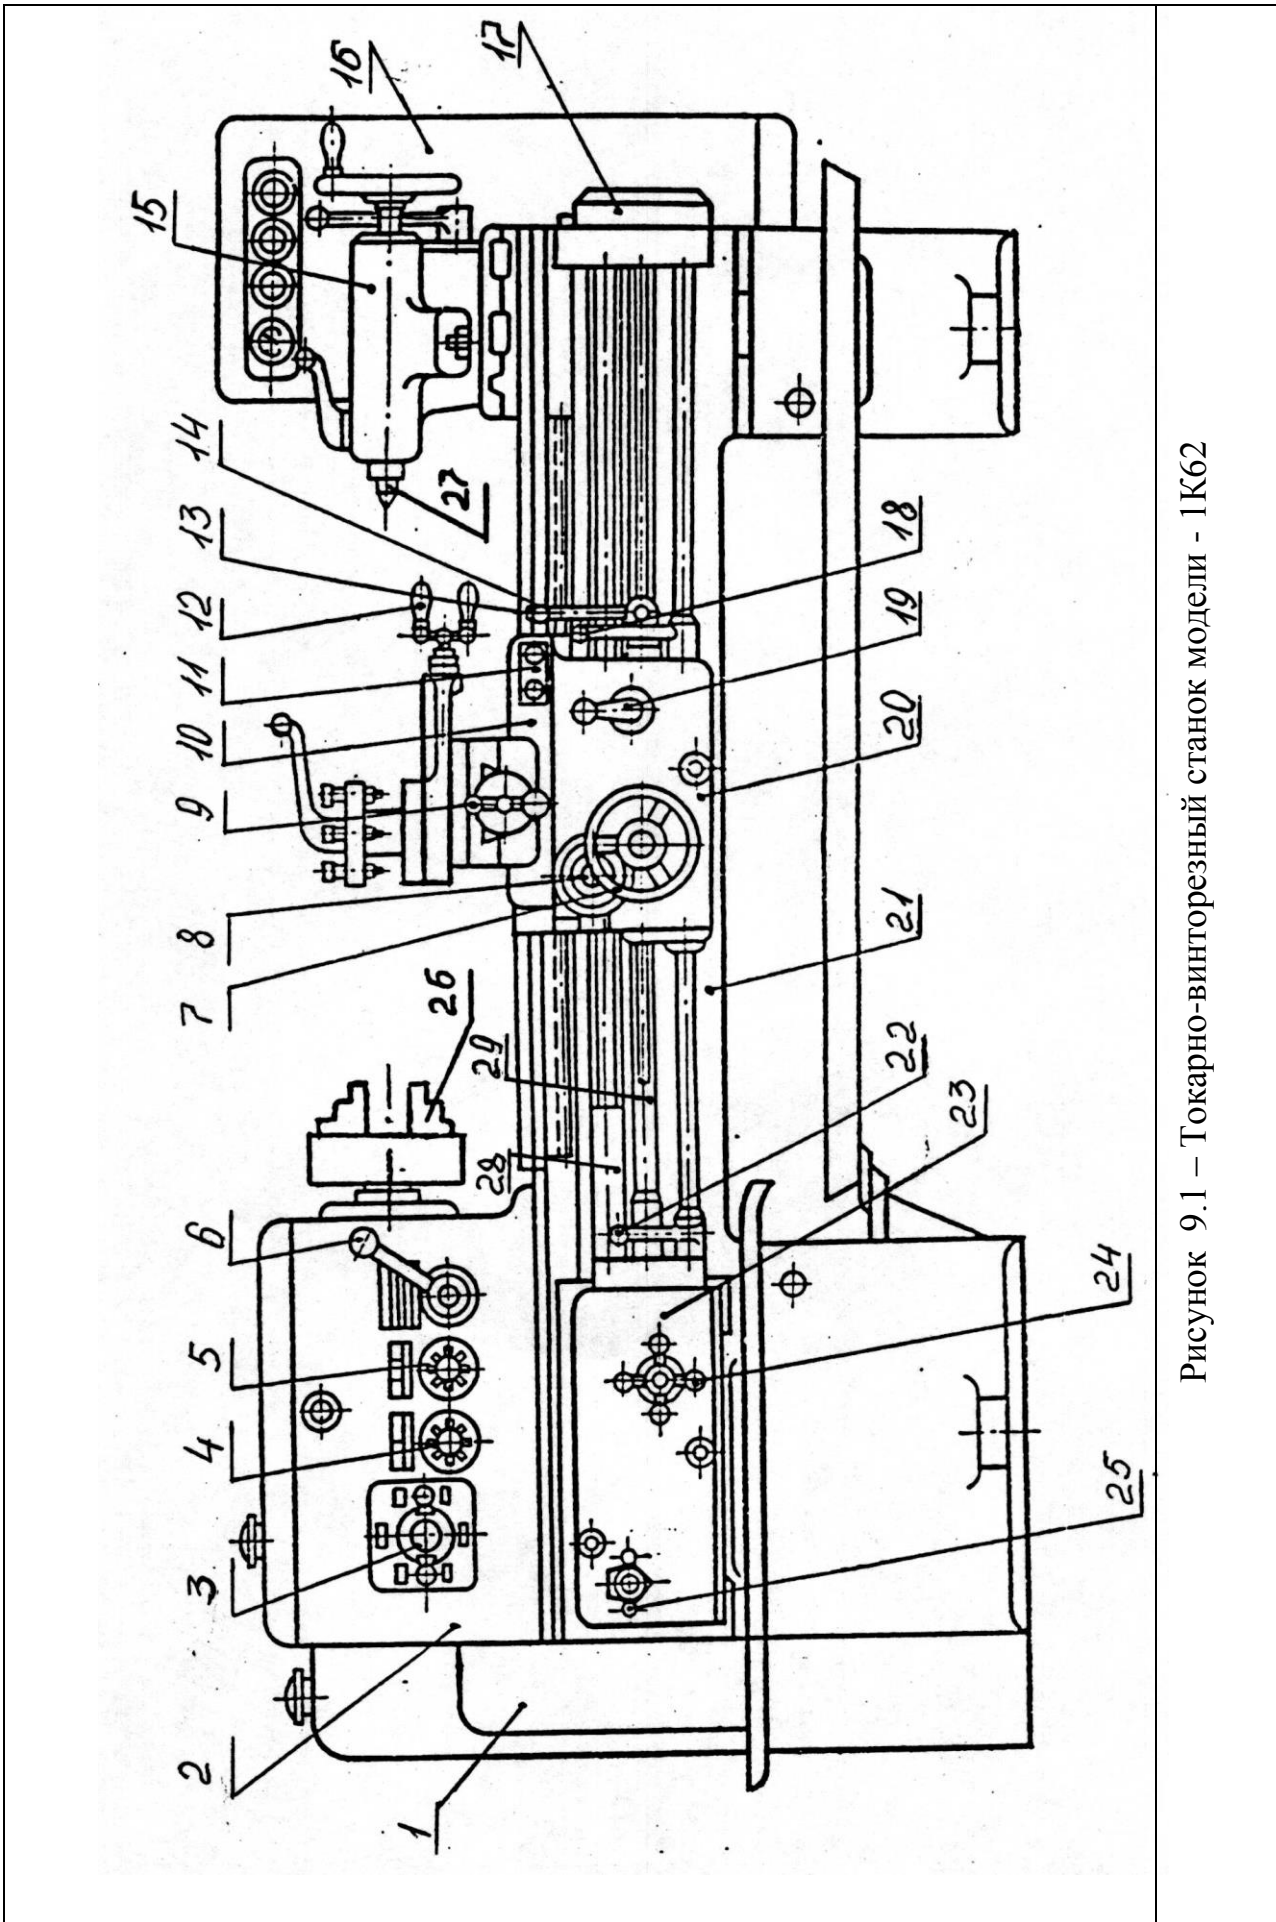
Токарно-винторезный станок модели - 1К62
